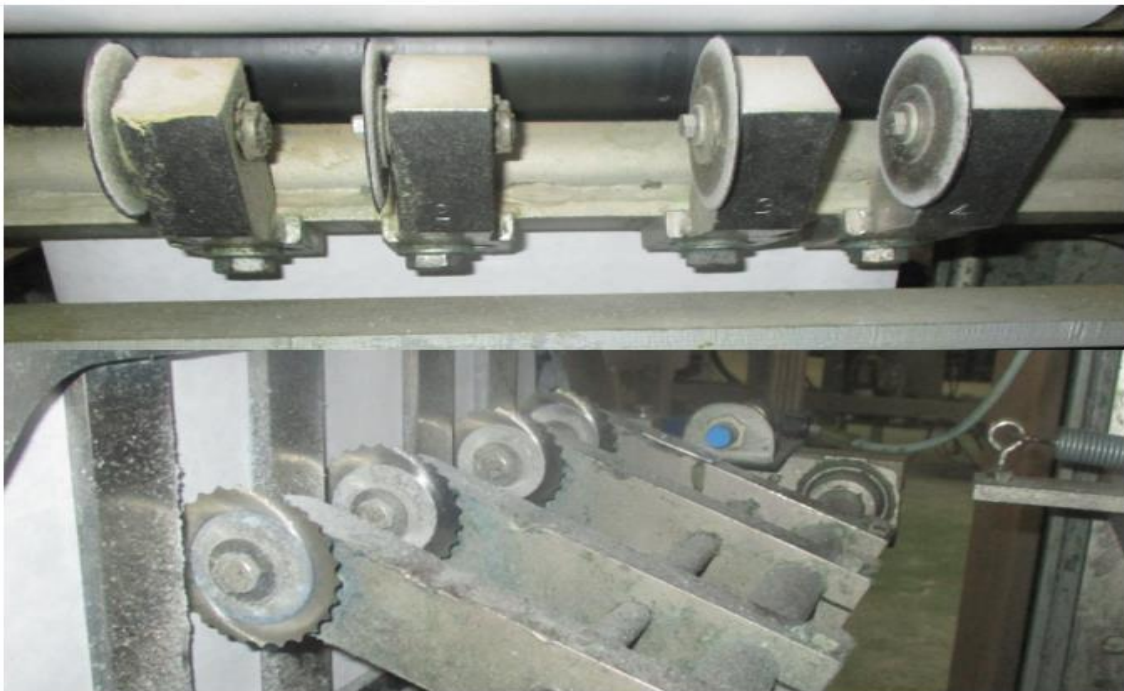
Conjunto de lâminas de corte de fundo do pacote.
